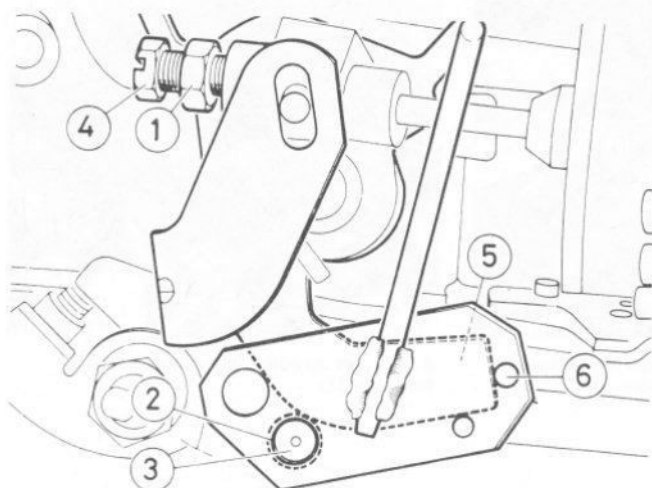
Réglage de l'OVAD - carburateur Weber 36 TLC (Sec 8)
